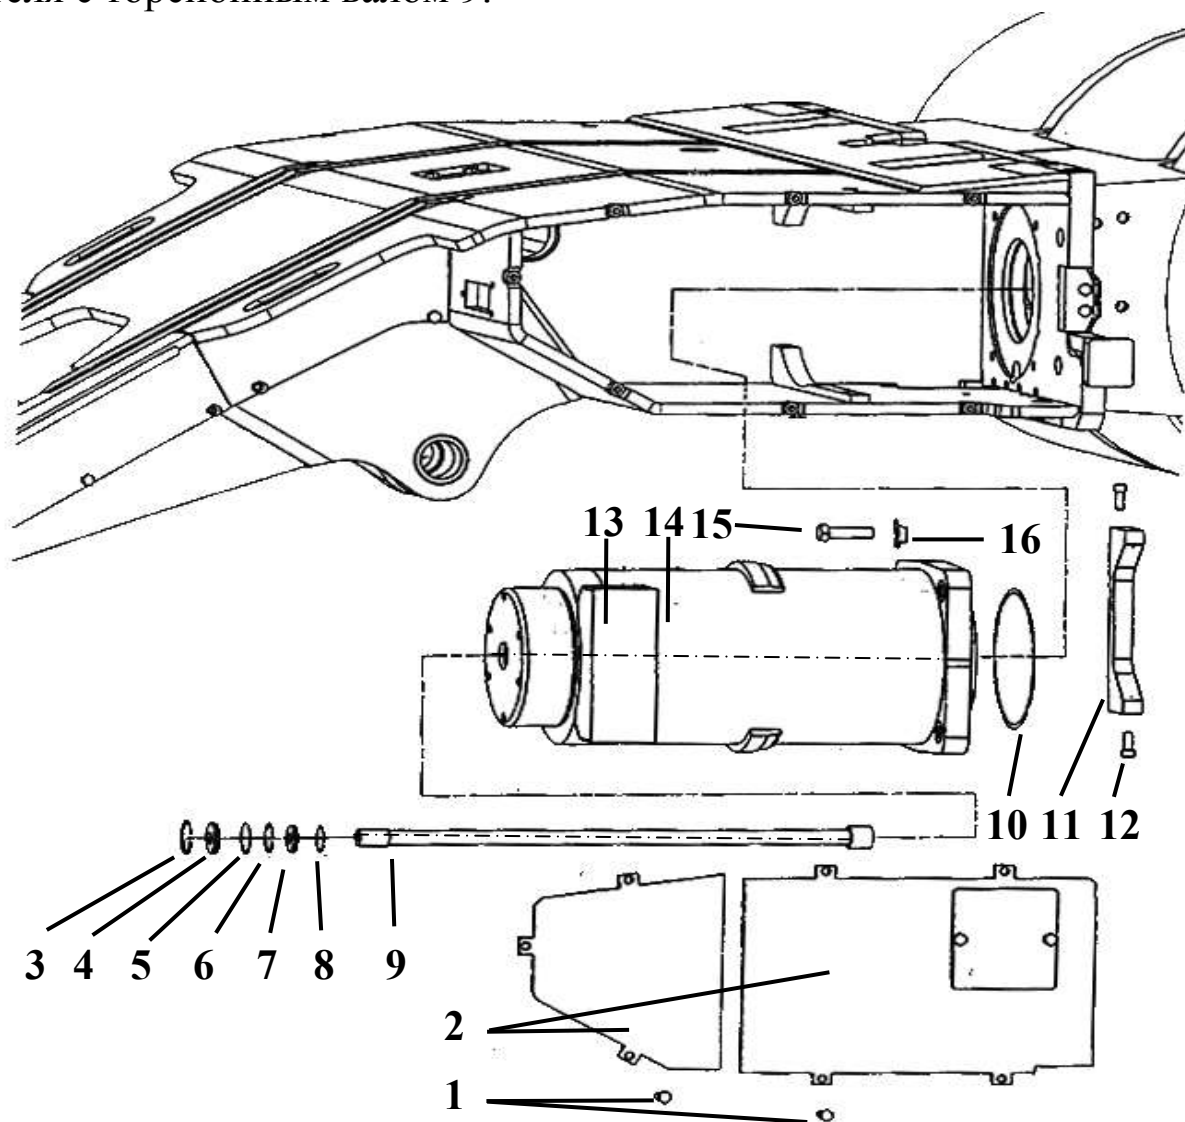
Компоновка правого электродвигателя врубового агрегата комбайна
